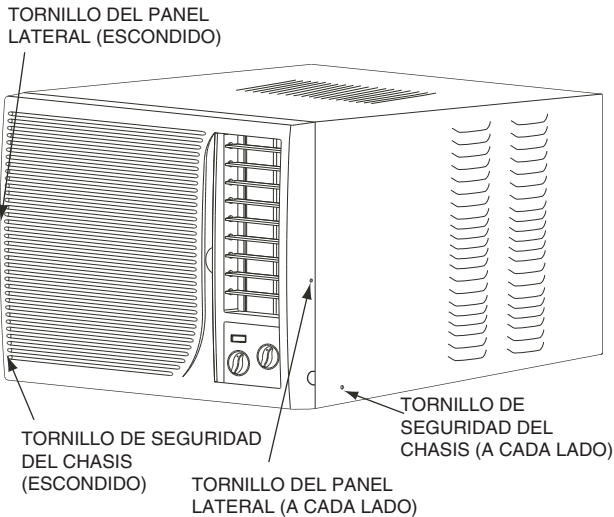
DESMONTAJE PANEL FRONTAL
